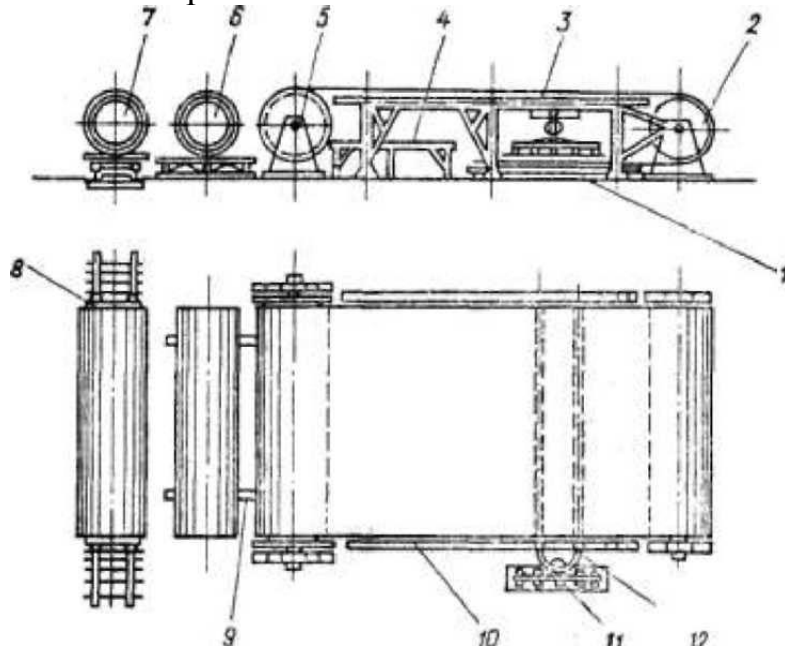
Схема двухъярусной установки для изготовления сварных листовых полотен методом рулонирования
